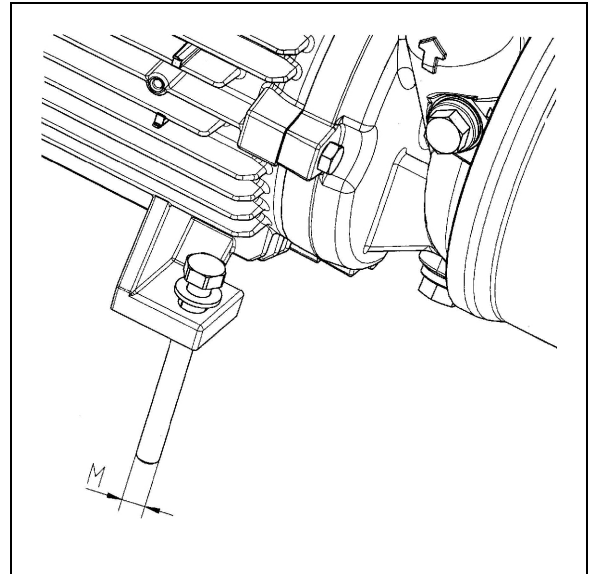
Elementi di fissaggio per avvitare i piedi al pavimento
